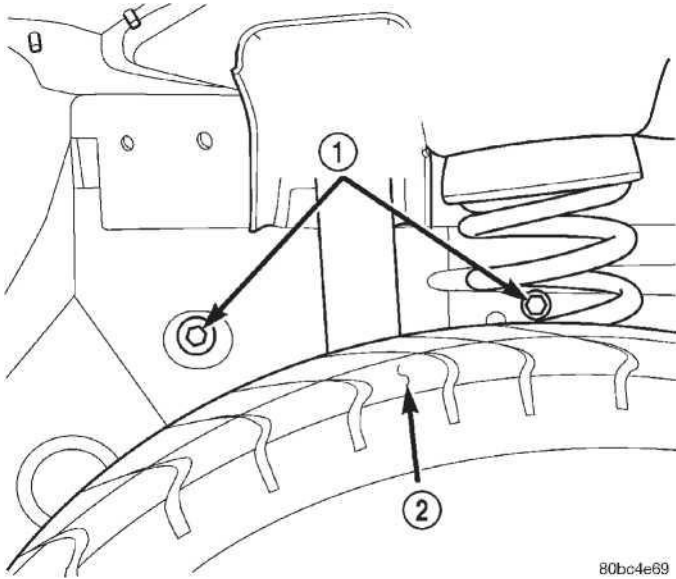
Болты пластины подоконника опоры двигателя - правильная ниша колеса
